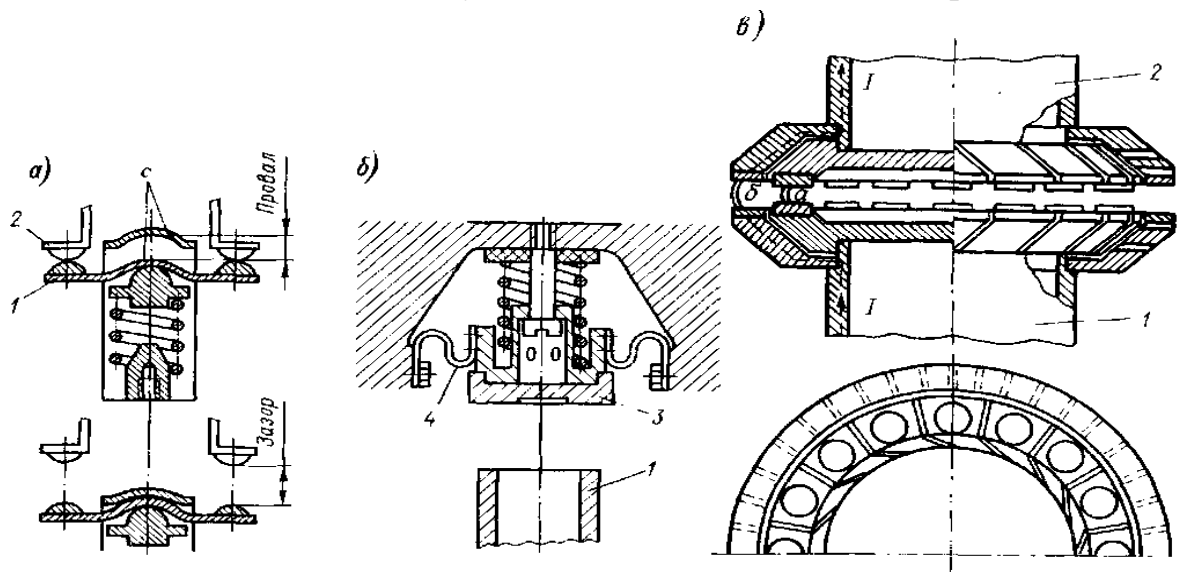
Торцеві контакти: а - мостиковий; б - торцевий; в - торцевий багатоточковий 1 - рухома контакт-деталь; 2 - нерухома контакт-деталь; 3 - нерухома контакт-деталь, яка переміщається на величину провалу; 4 - гнучкий зв'язок
